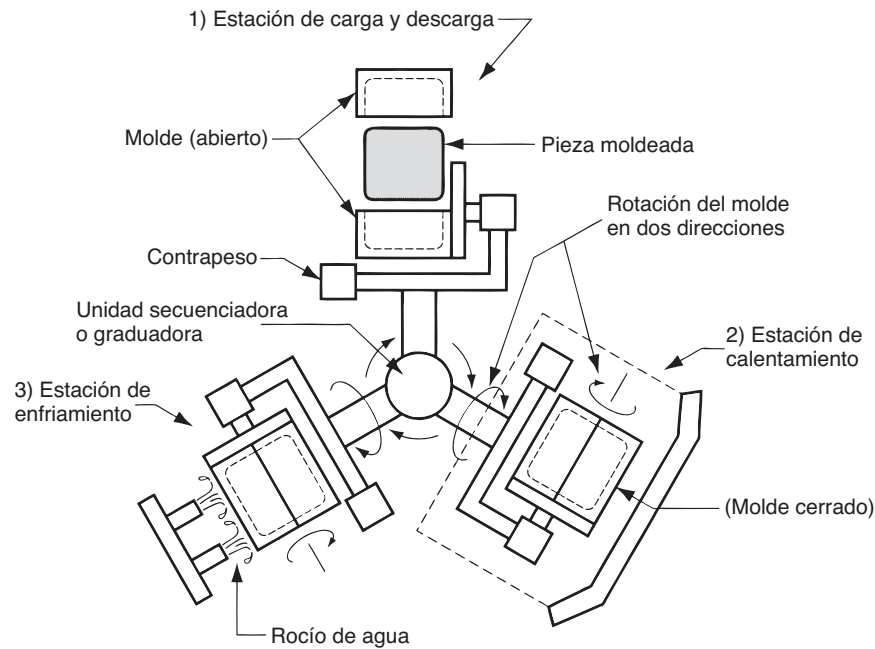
Ciclo de moldeo rotacional ejecutado sobre una máquina indizadora de tres estaciones: 1) estación de carga y descarga; 2) el molde se calienta y gira; 3) enfriamiento del molde.
